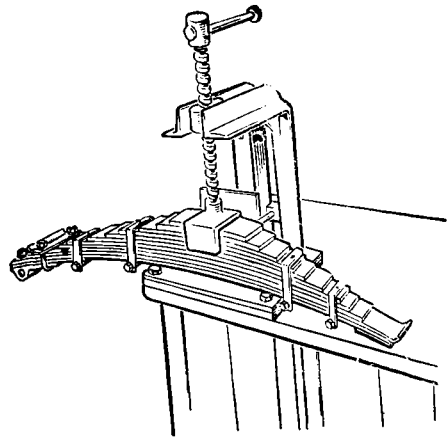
Сборка (разборка) рессор на специальном приспособлении
